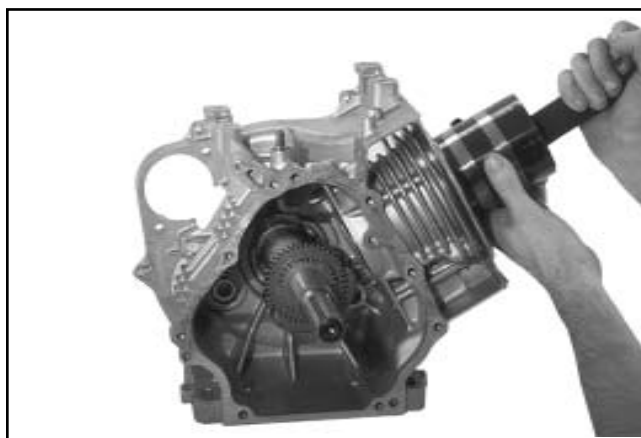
Installazione del pistone con il compressore per segmenti.
